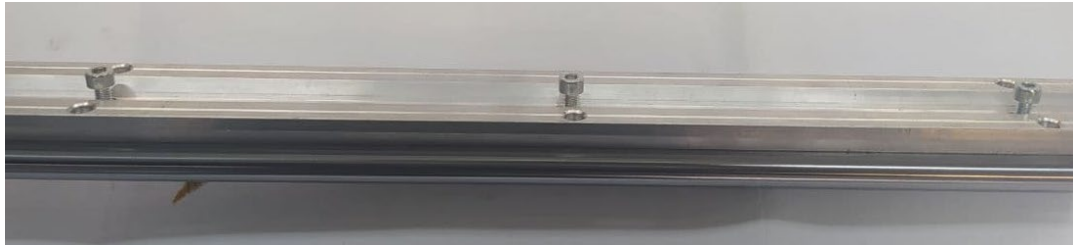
Лінійний вал з опорою з'єднані гвинтами
